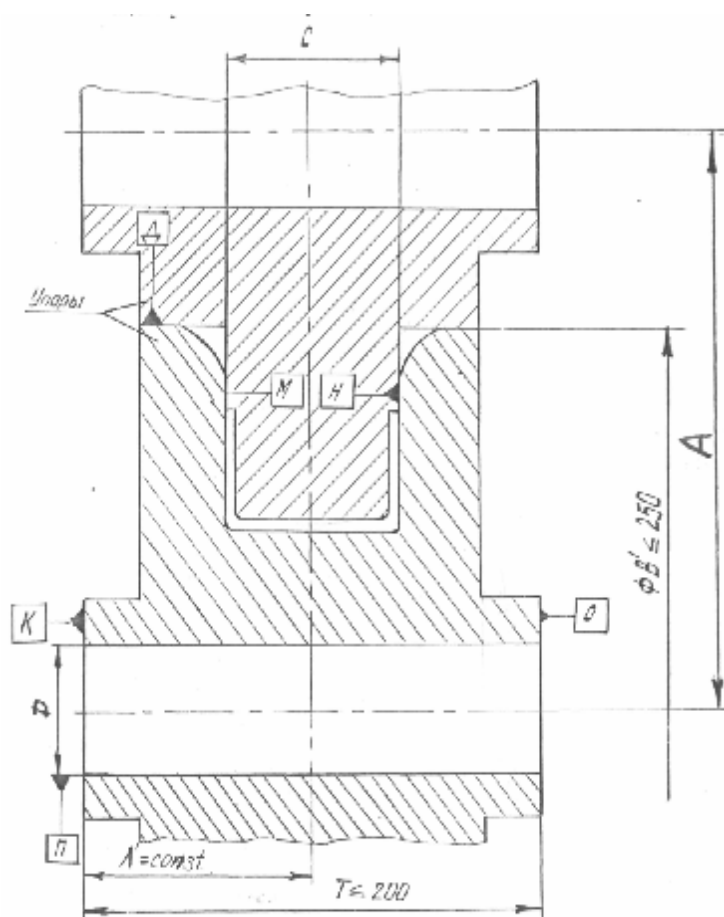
Схема расположения установочных баз формирующих роликов: Д, Л, М, К, П – установочные базы
